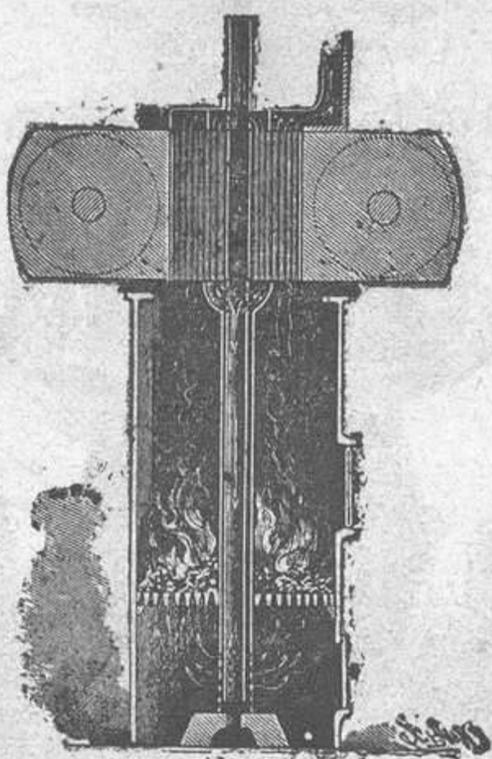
SECCIÓN LONGITUDINAL DEL MOTOR.
